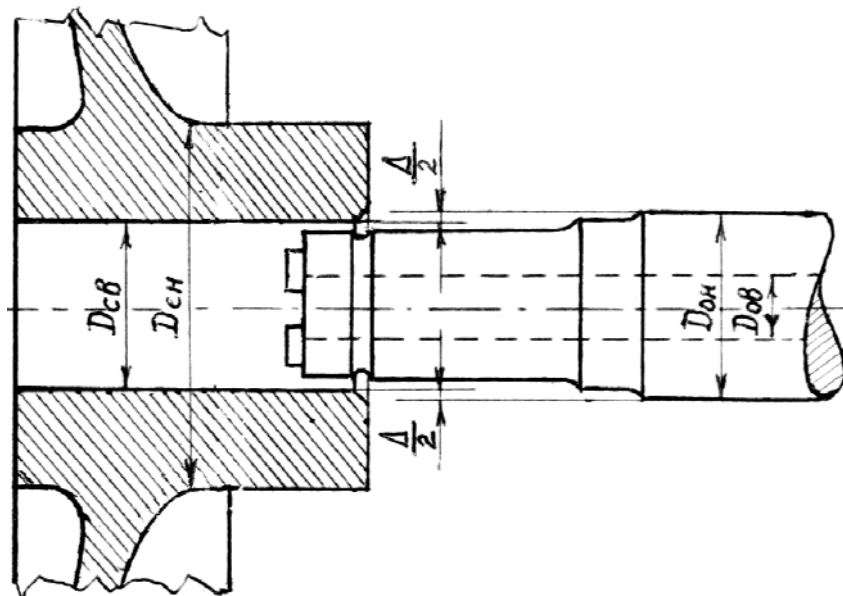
Розрахункова схема пресового з'єднання «вісь–колісний центр»
